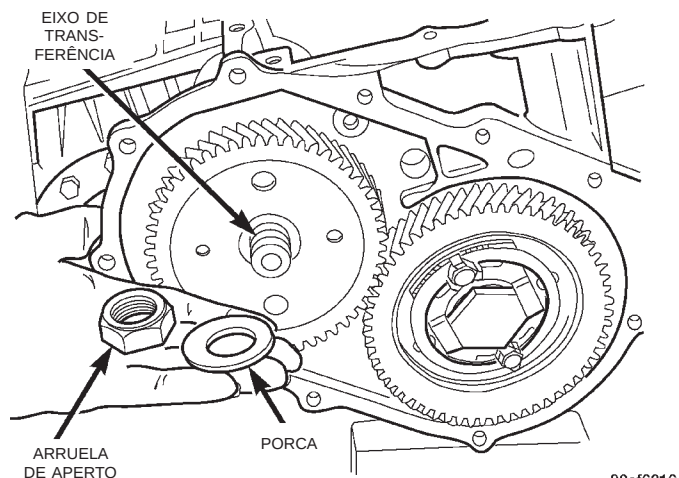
Proca da Engrenagem do Eixo de Transferência e Arruela Cônica
